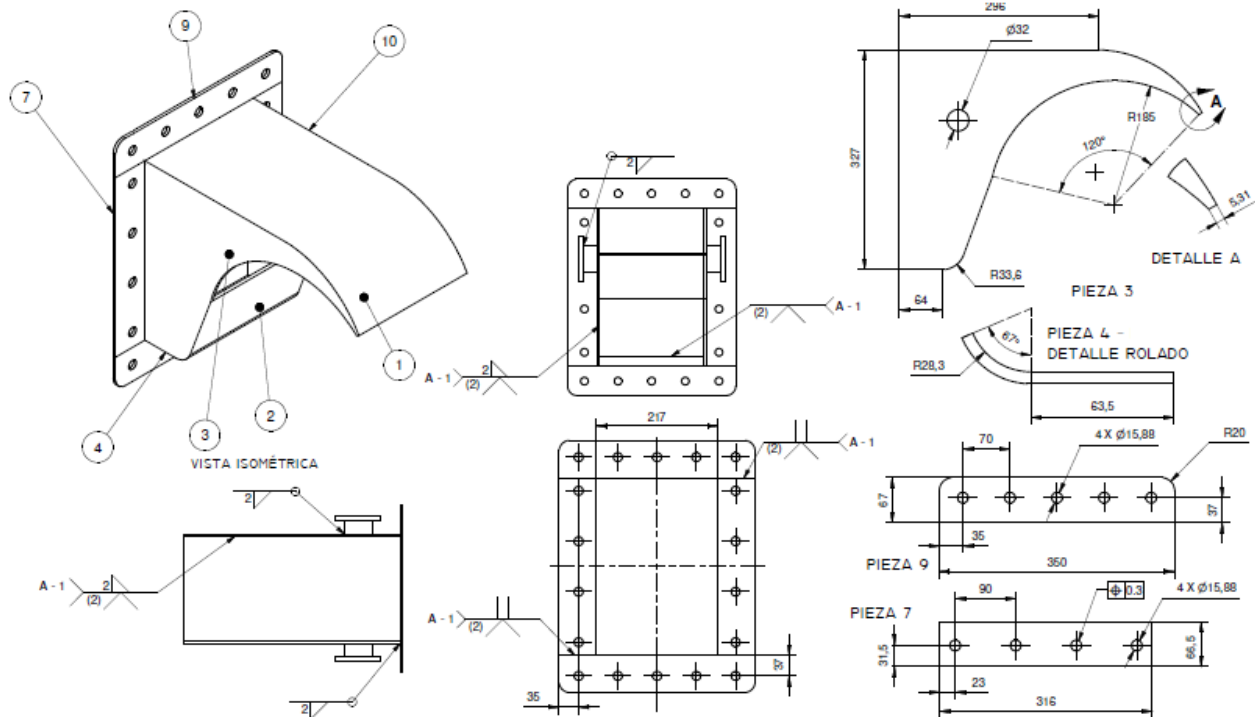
Plano de ensamble soldado: Inyector. Detalle de componentes, incluyendo brida.
